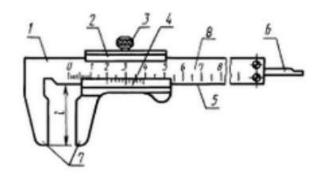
Штангенциркуль односторонний с глубиномером с измерительными поверхностями из твердых сплавов
